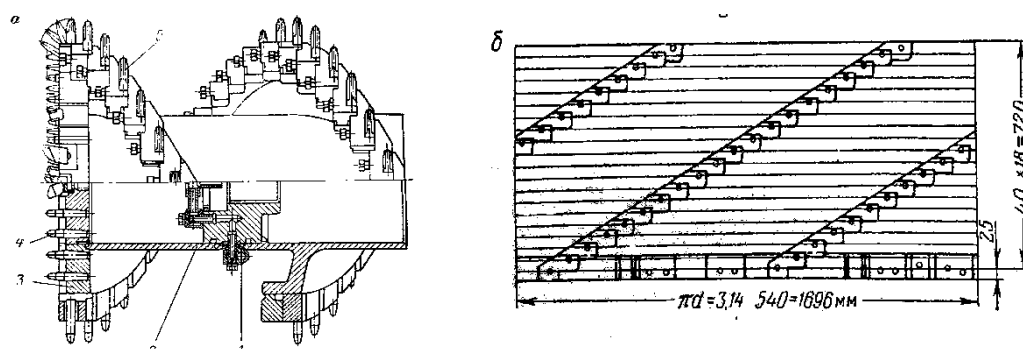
Общий вид шнека и схема установки резцов
